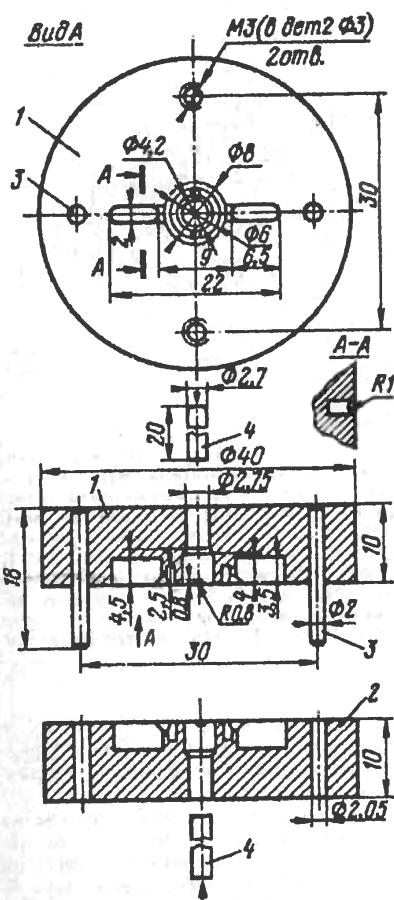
Пресс-форма для изготовления морданного подвеса звукоснимателя: 1 — крышка, Д16-Т; 2 — основание, Д16-Т; 3 — направляющая ст. З, 3 шт., запрессовать в дет. 1; 4 — стержни, ст. З, 2 шт.
